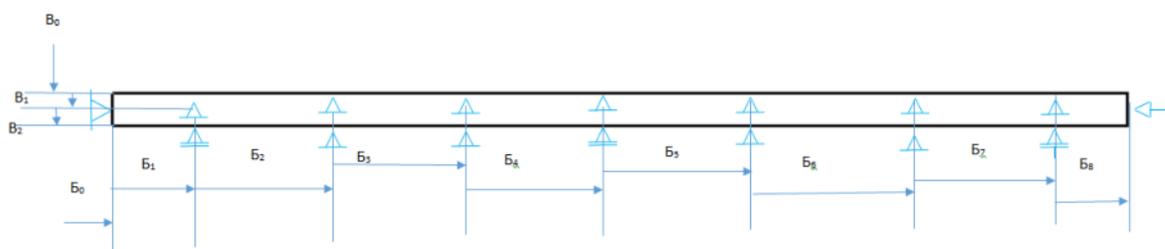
Размерная цепь разрабатываемого приспособления
